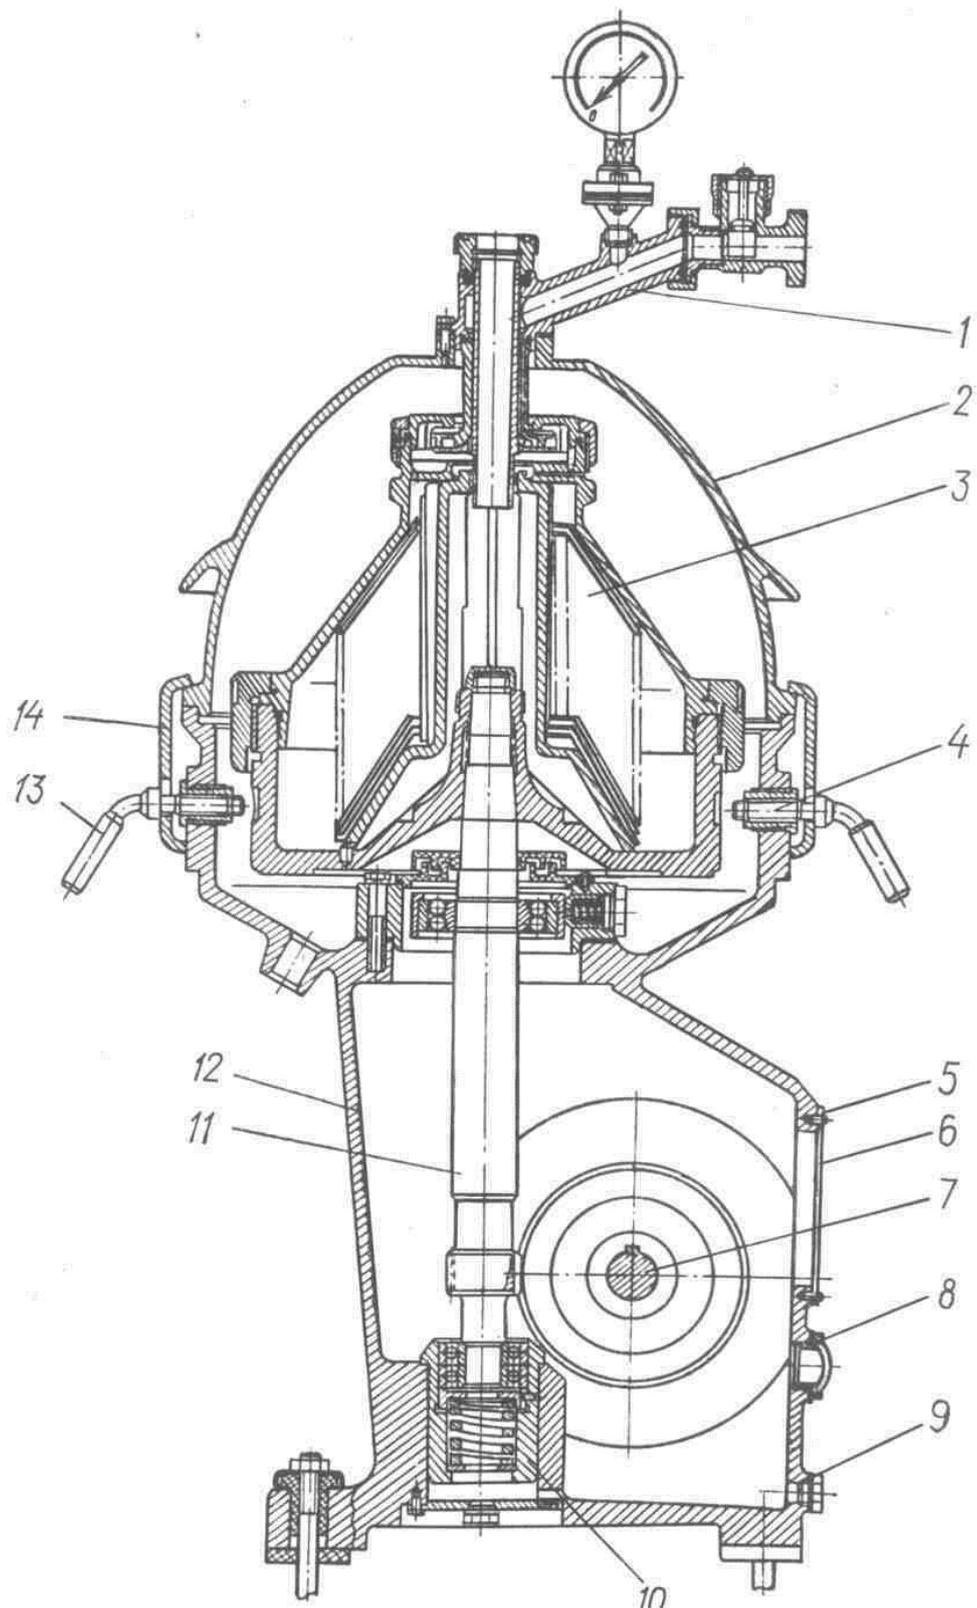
Сепаратор-молокоочиститель ОМА-3М: 1 – приемно-отводящее устройство; 2 – колпак; 3 – барабан; 4, 13 – упоры; 5 – прокладка; 6 – крышка 7 – горизонтальный вал; 8 – указатель уровня масла; 9 – пробка спуска масла; 10 – нижняя опора вертикального вала; 11 – вертикальный вал; 12 – станина; 14 прижимная планка
